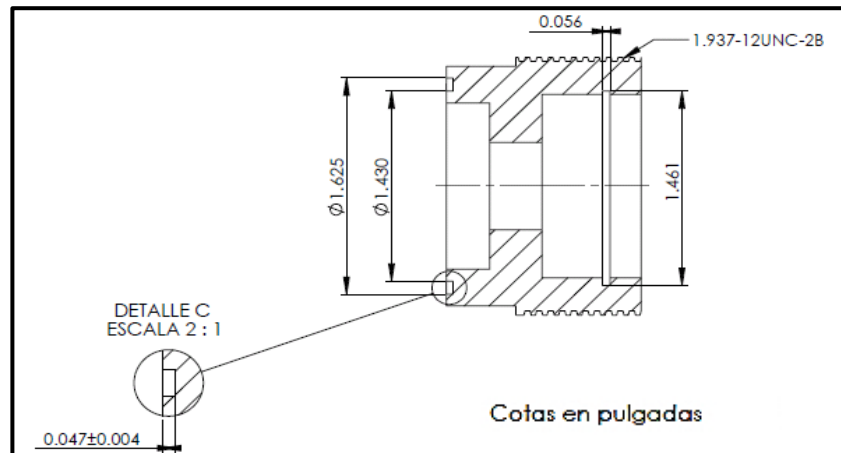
Dimensiones del portasello mecánico segunda parte.
